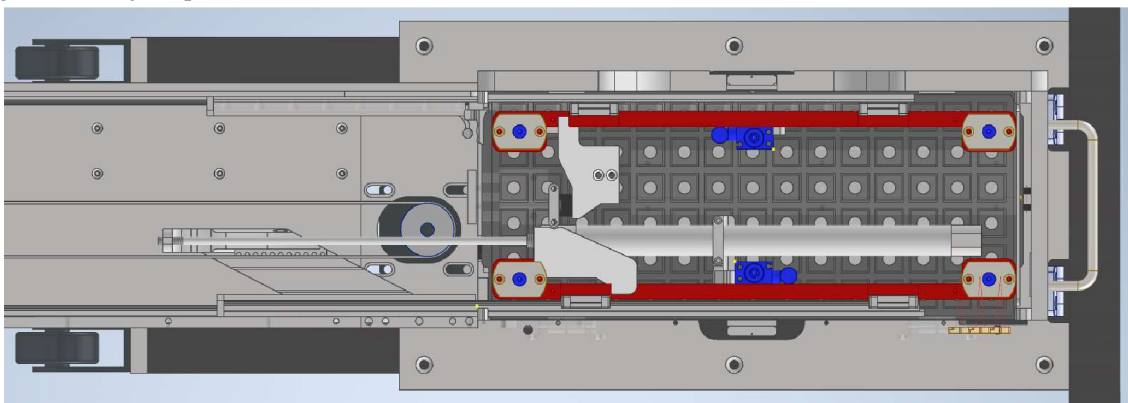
Umístění pístu posuvu druhého stupně dopravníku
